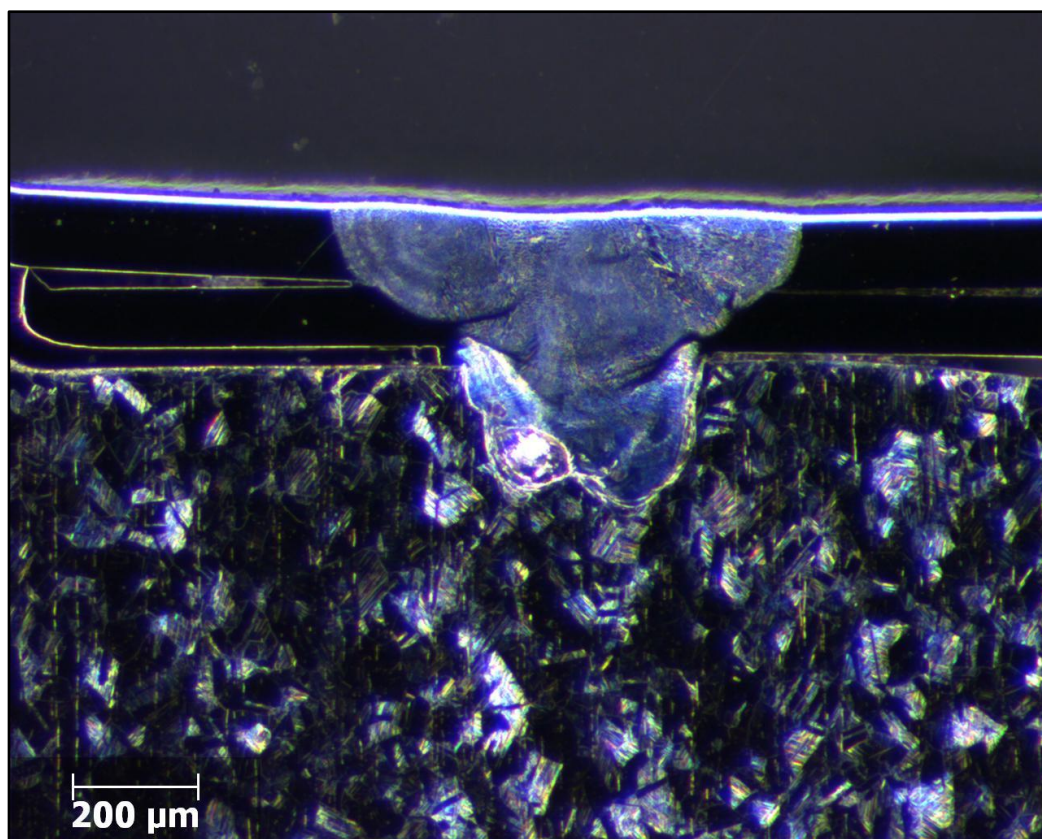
Die Schweißnaht wie in Abb. 7 unter dem Stereomikroskop – 100 x
